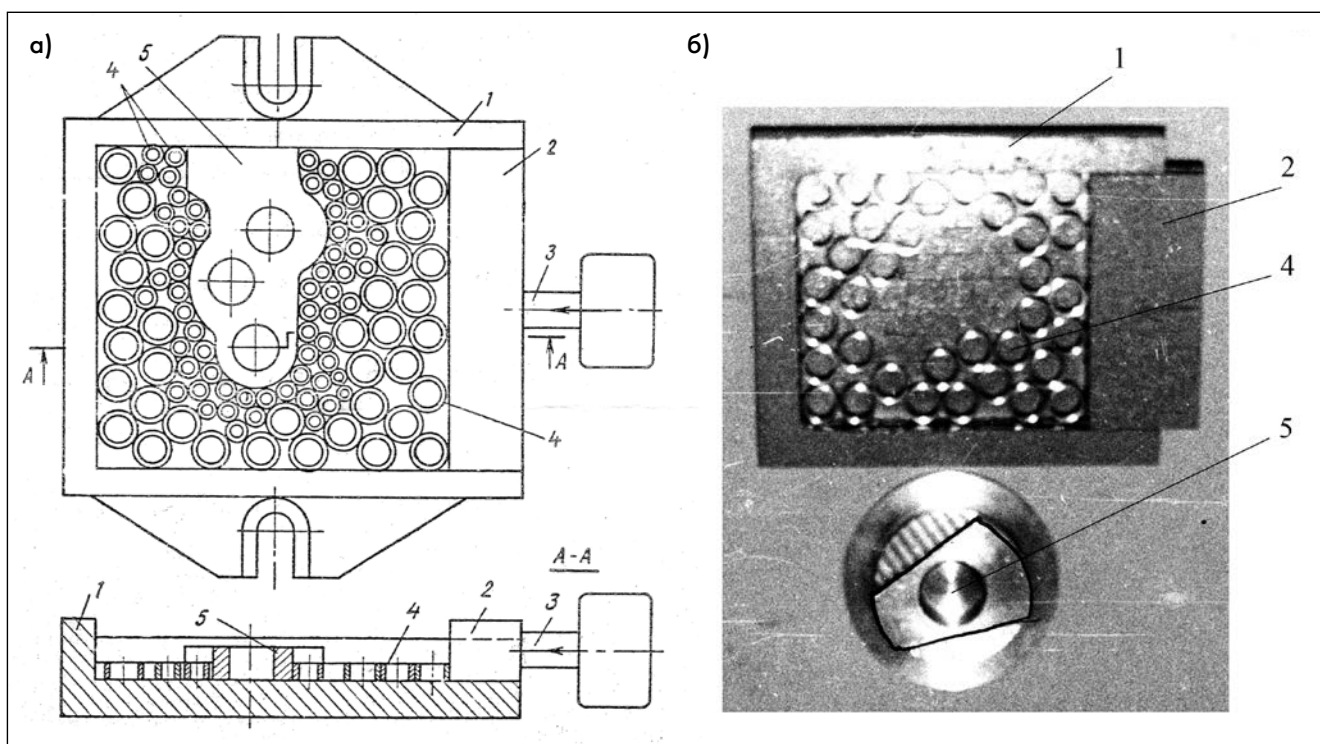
Тиски с кольцами: а) конструкция, б) общий вид
